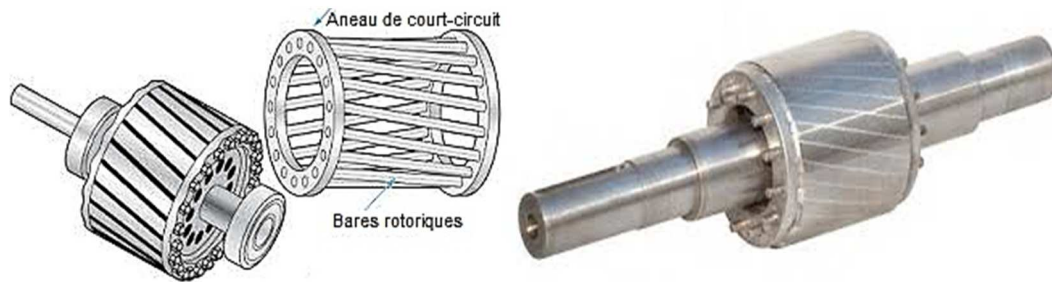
Rotor de la machine asynchrone à cage d'écureuil.
